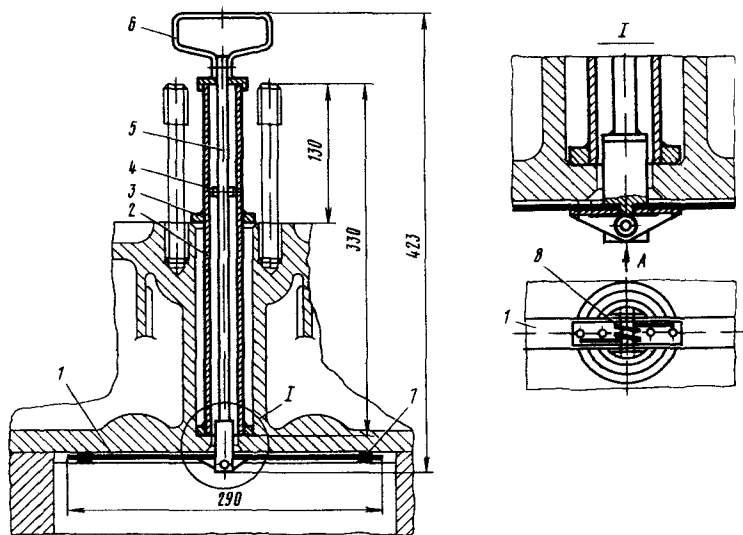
Приспособление для измерения линейной величины камеры сжатия дизеля Д50
